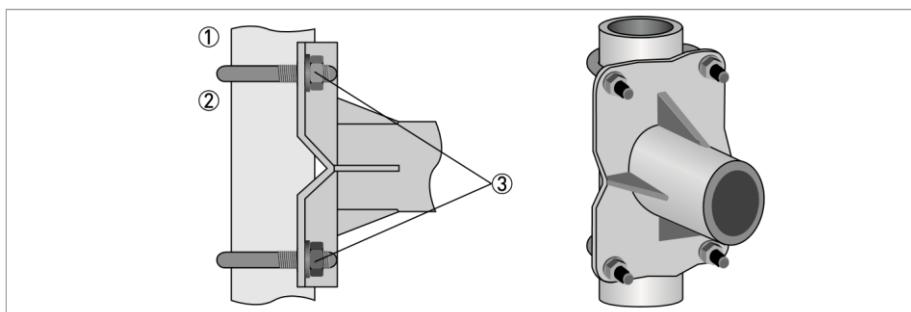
Крепление корпуса конвертера полевой версии
